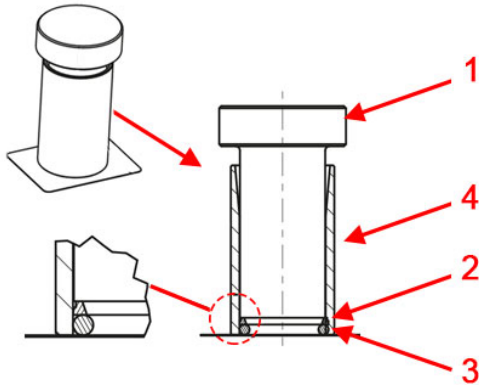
O-Ring im Montagewerkzeug positionieren
